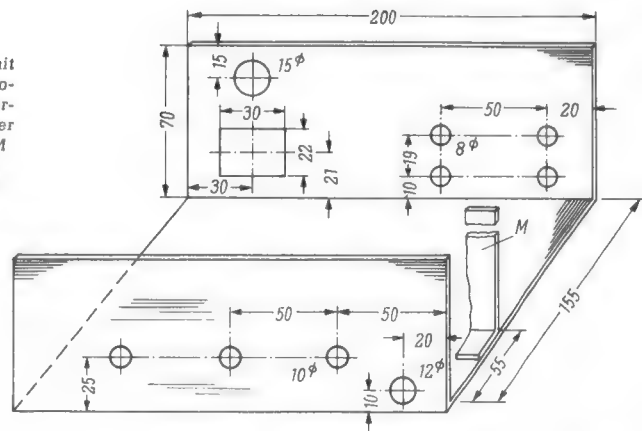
U-förmige Verschlusshaube für den Trägerteil nach Bild 9. Die Innenflanschen an den Schenkeln dienen mit ihren Bohrungen zum Befestigen der Haube am Trägerteil
